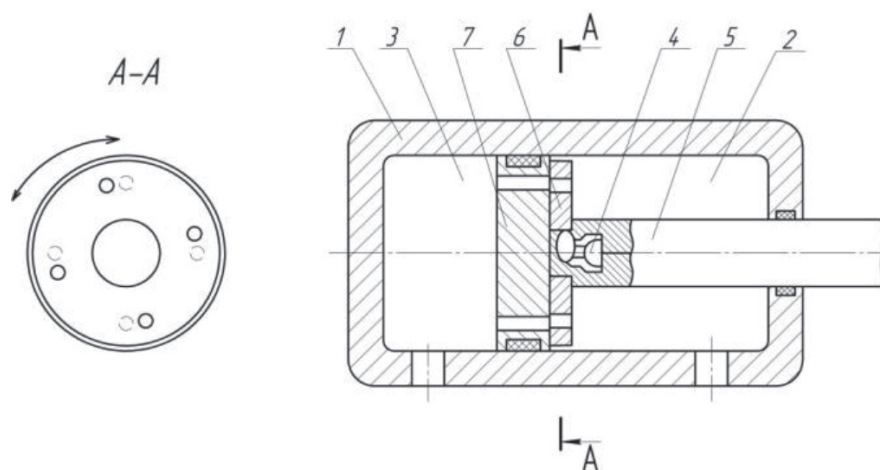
Конструкция гидроцилиндра с подвижной частью поршня
